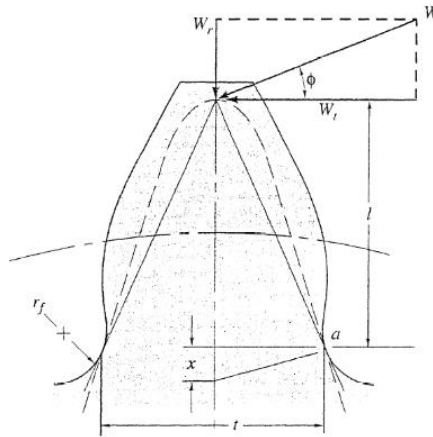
Fuerzas tangenciales y radiales en los engranajes [22]
